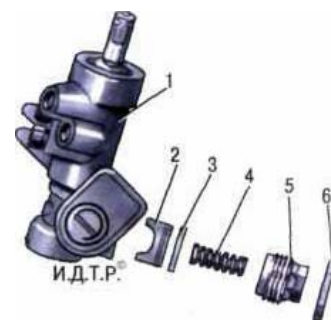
Регулировочный узел рулевого механизма: 1 - картер рулевого механизма; 2 - плунжер; 3 - уплотнительное кольцо; 4 - пружина; 5 - регулировочная пробка; 6 - контргайка
